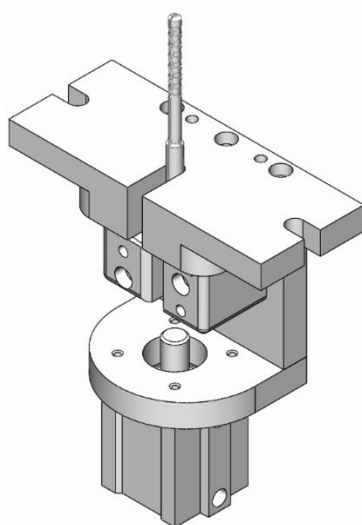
3D-модель приспособления для сборки дюбеля
